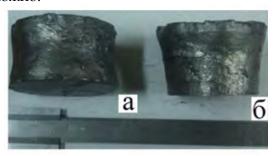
Общий вид полуфабрикатов после деформирования разгонкой одного торца (б) и двух торцов (а) цилиндрической заготовки
